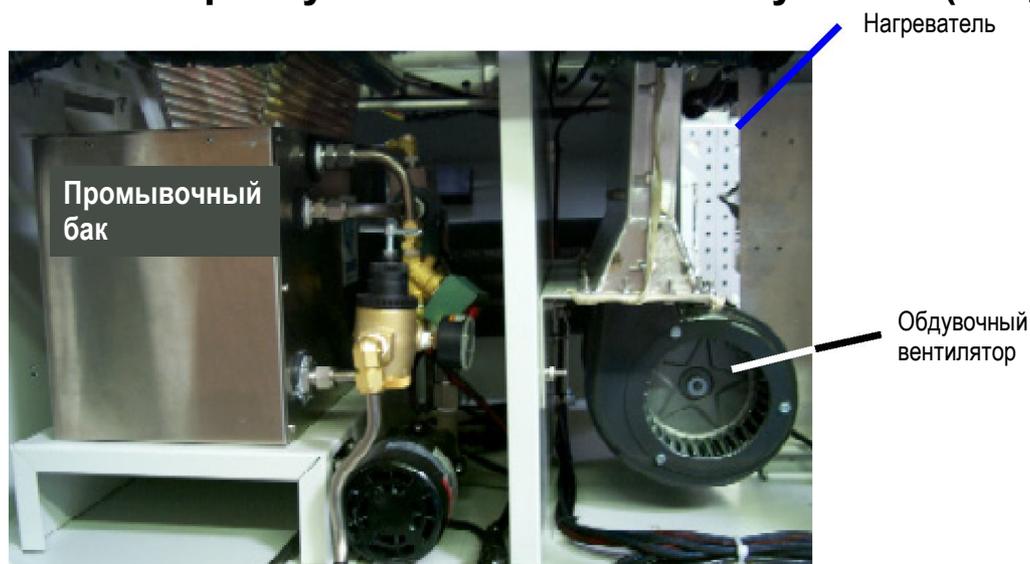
Установка ультразвукового очистителя и сушилки
